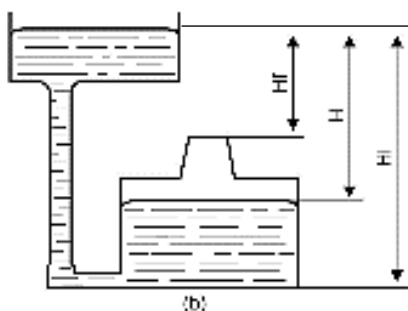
Enchimento por baixo. Adaptado de Baldam, 2014.
